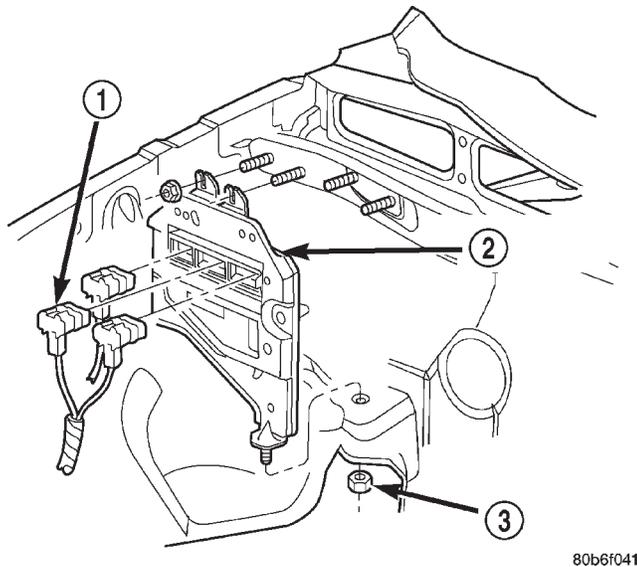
32-polige Steckverbinder, Computer/Motorsteuerung (PCM)
